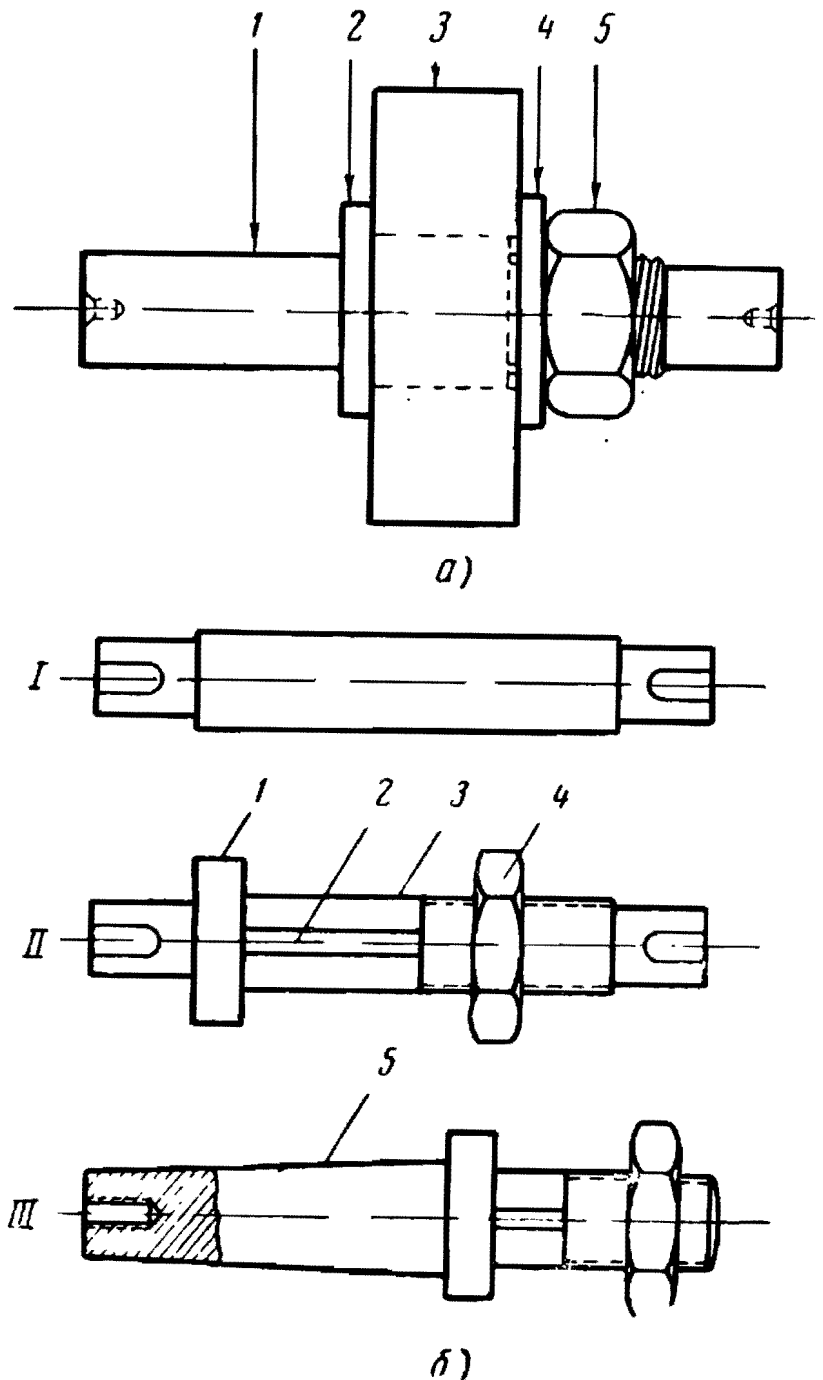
Установка и закрепление заготовки зубчатого колеса (а) и оправки для установки и закрепления заготовки зубчатого колеса (б)
